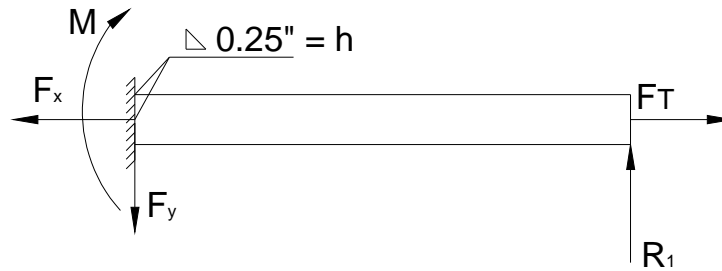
Reacciones sobre la soldadura del triángulo de tiro.
